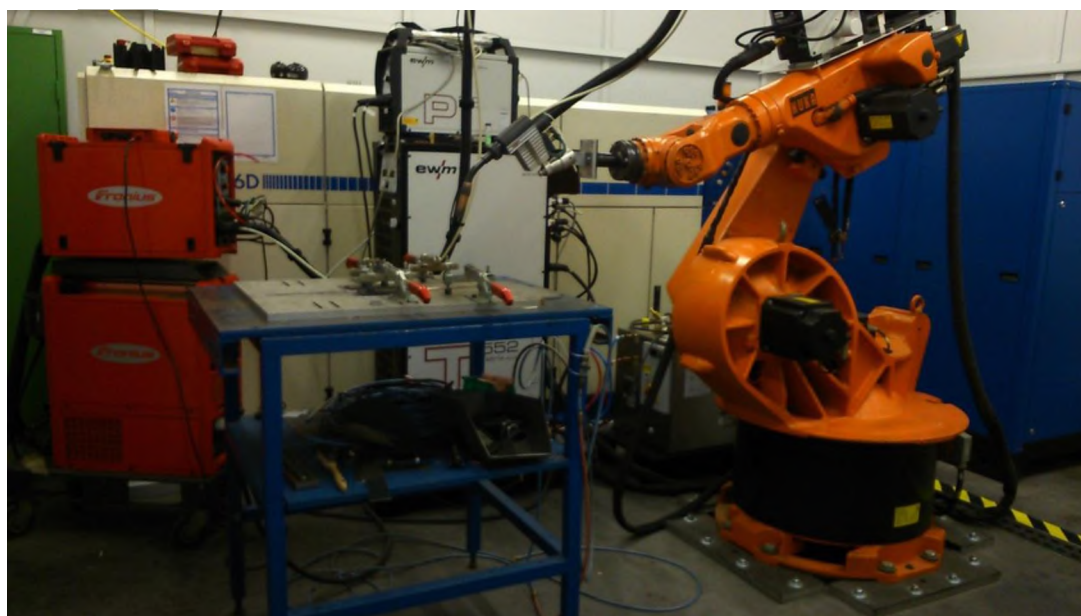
Сварочная установка ISAF с техникой СМТ
